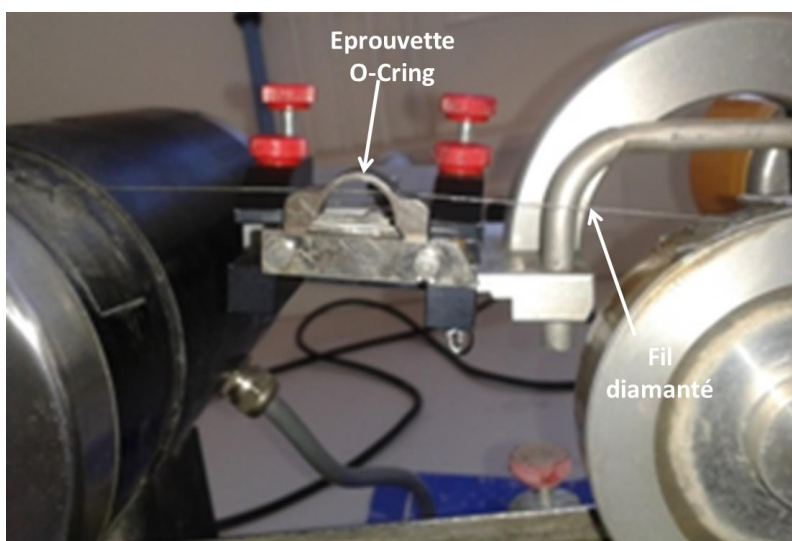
Découpage à la scie à fil diamantée des éprouvettes OCR
